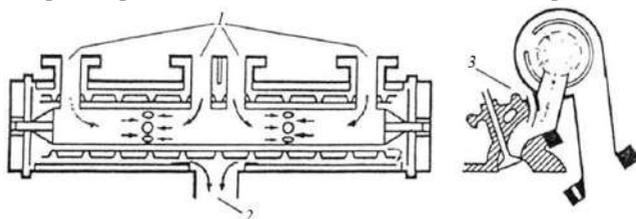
Термічний нейтралізатор-дожигатель:
